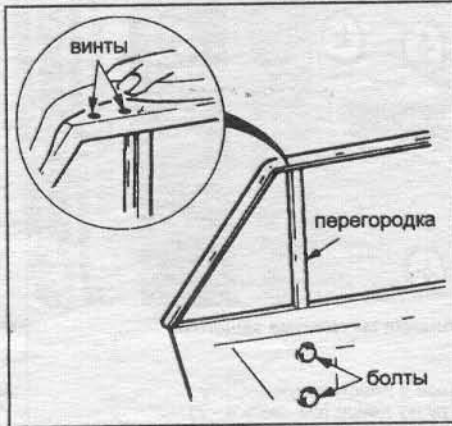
Крепление неподвижного стекла и разделительной перегородки задней двери.
